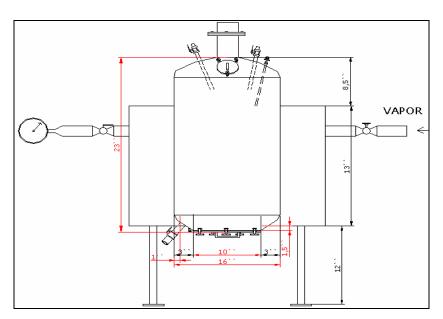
Vista frontal del diseño entregado al soldador para su modificación.
